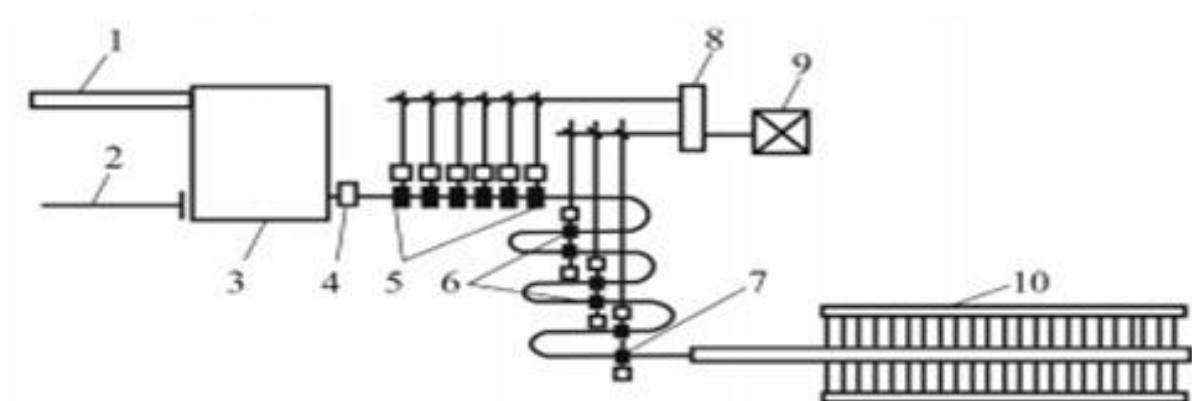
Схема расположения основного оборудования полунепрерывного мелкосортно-проволочного стана: 1 - загрузочный рольганг; 2 - выталкиватель заготовок; 3 - нагревательная печь; 4 - вытаскиватель заготовок; 5 - черновая группа клетей; 6 - промежуточная группа клетей; 7 - чистовая группа клетей; 8 - редуктор; 9 - электродвигатель; 10 - холодильник
